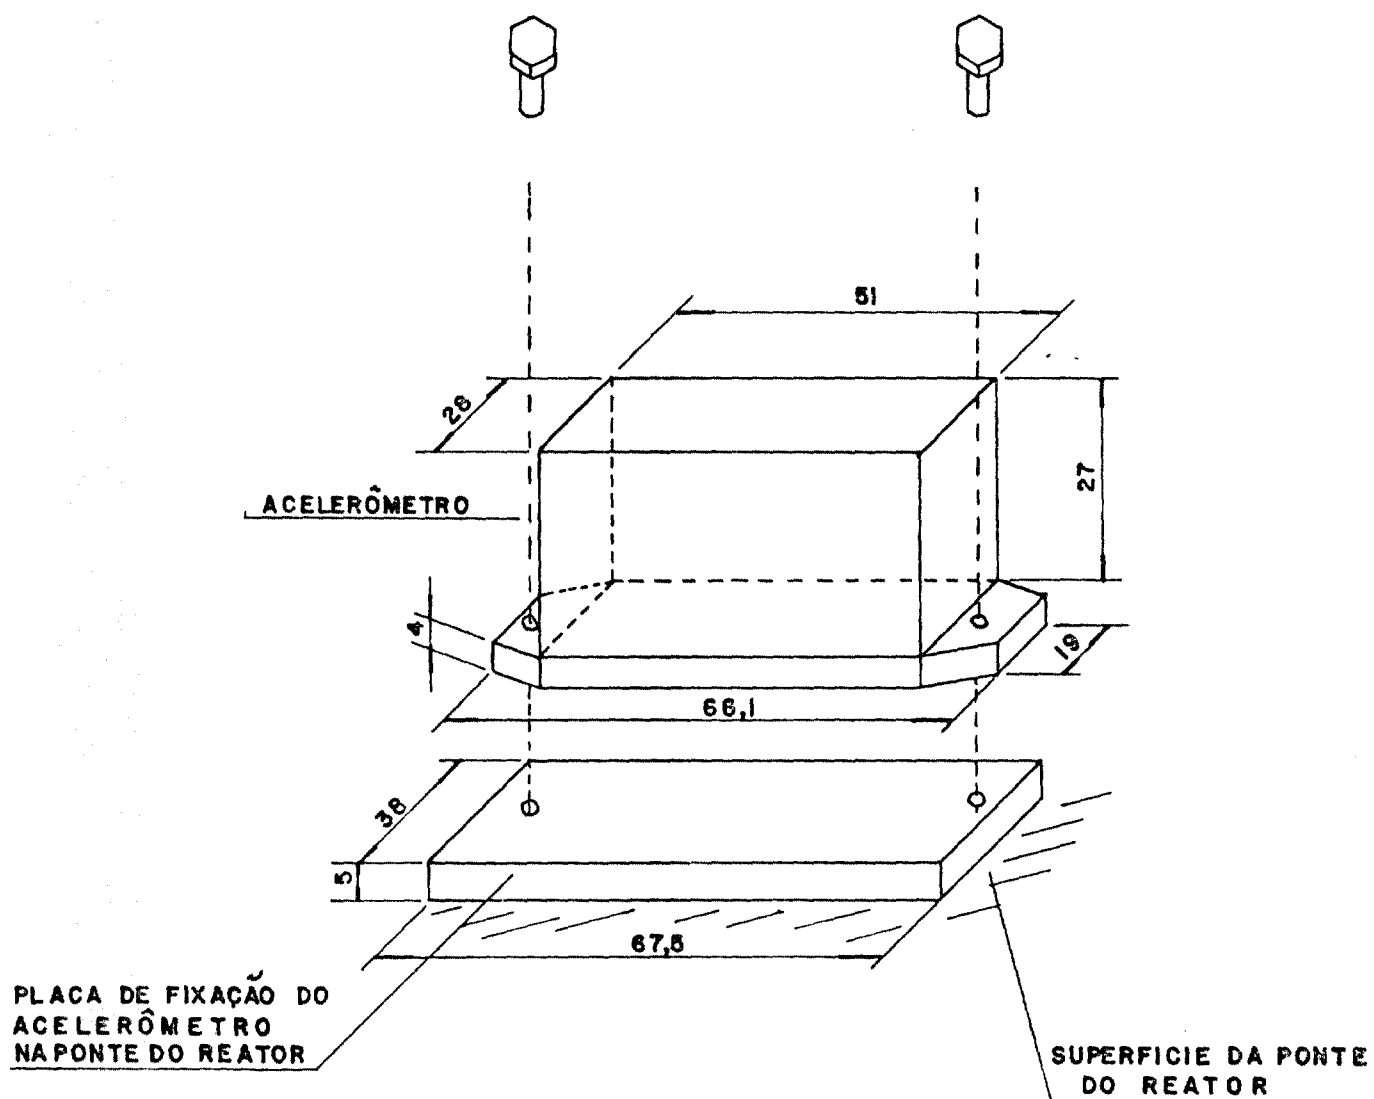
Sistema de Fixação do Acelerômetro à Placa forma do Reator IEAR-1. (Dimensões em mm).
